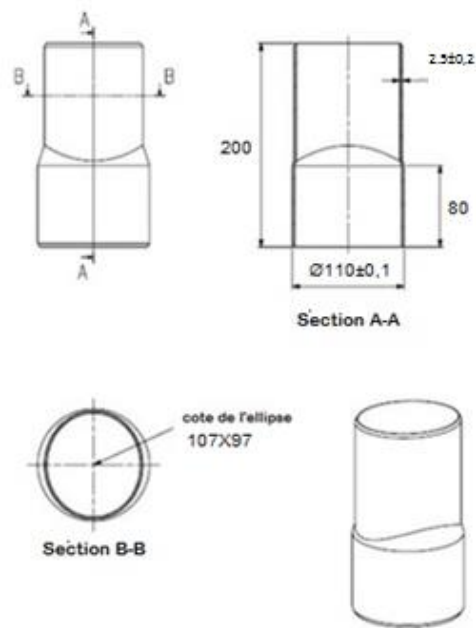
Calibre pour essai d'étanchéité à l'eau pour simuler la sortie des appareils sanitaires (dimensions en mm)
